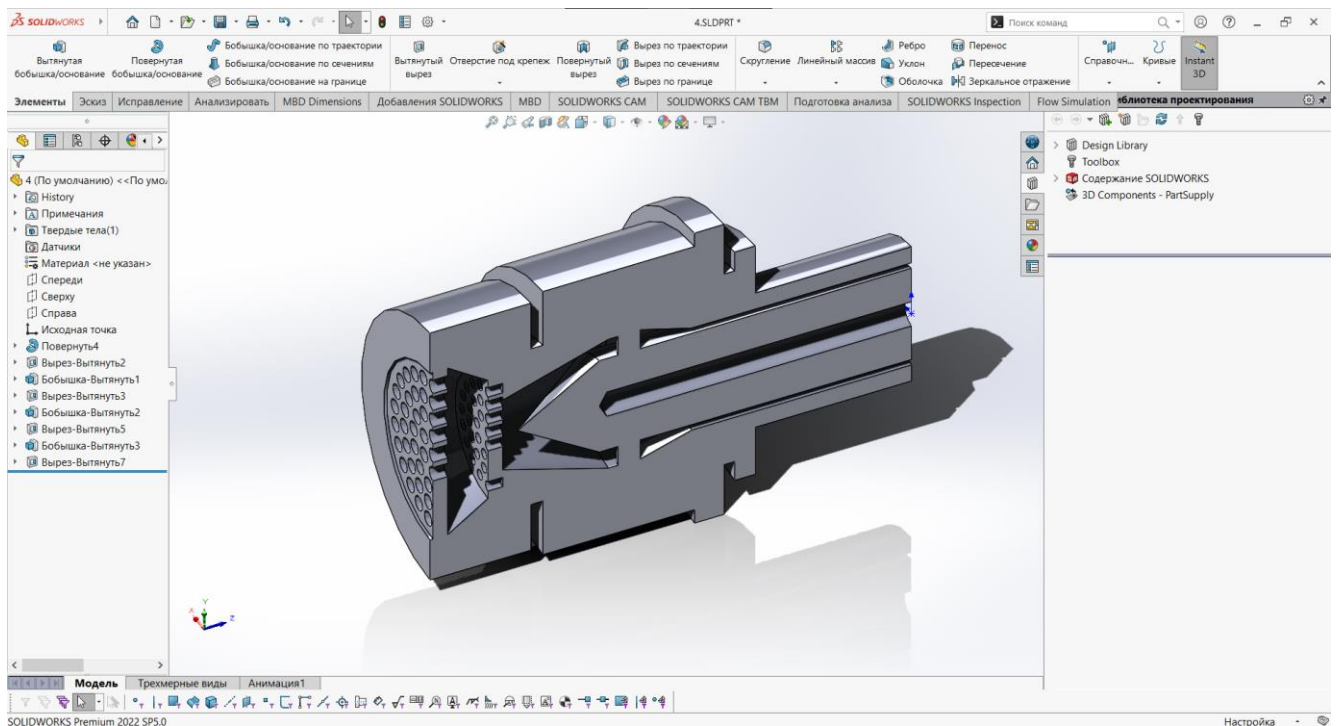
3D-модель модернізованої конструкції формуючої головки в розрізі
